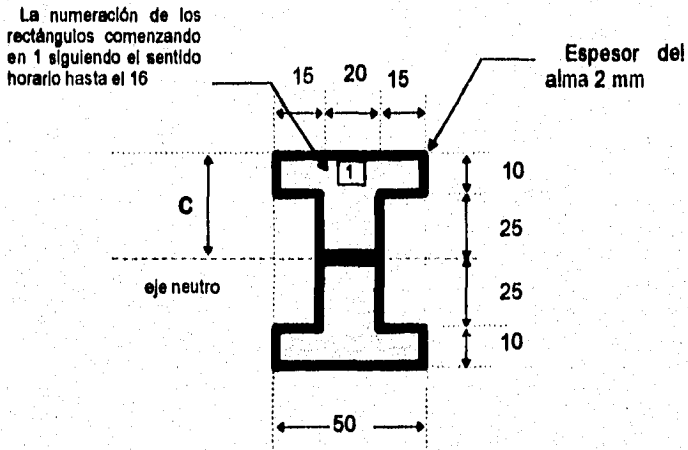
Sección transversal de la viga compuesta "I". [cotas en milímetros]
